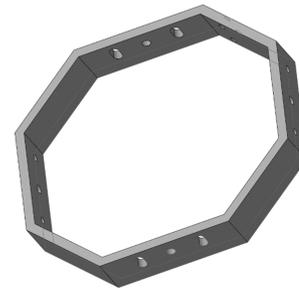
Главный корпус юстировки в вертикальной плоскости зеркала
